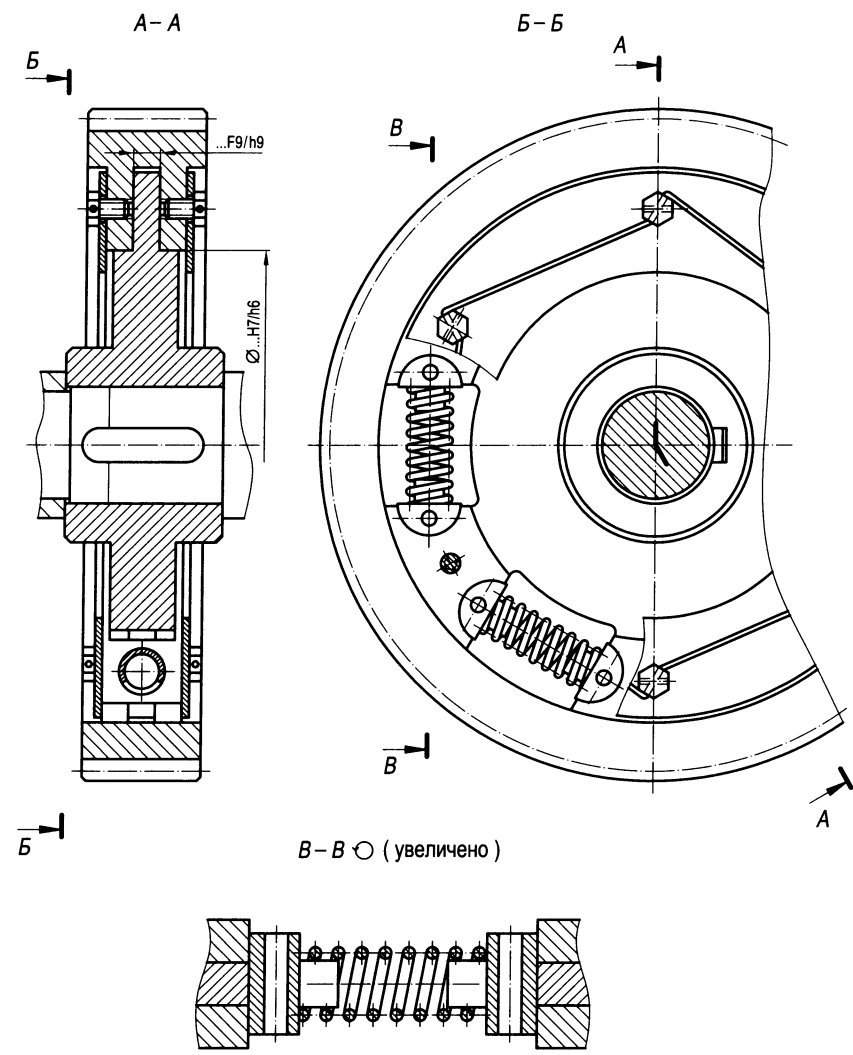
2. Эскизы промежуточного вала и зубчатого колеса с пружинами сжатия
